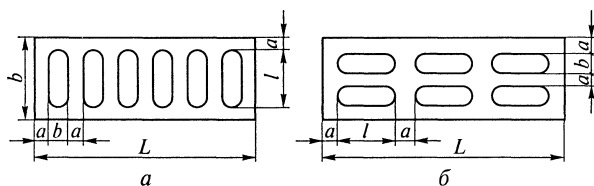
Расположение тестовых заготовок на льюлке печи:
